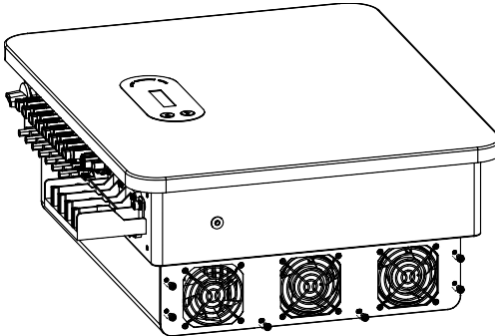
Entfernen Sie die sechs Schrauben von der Lüftergrundplatte
